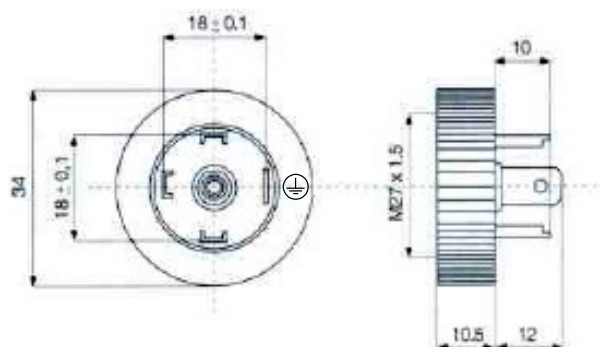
База для герморазъёма DIN 43650, форма А круглая
